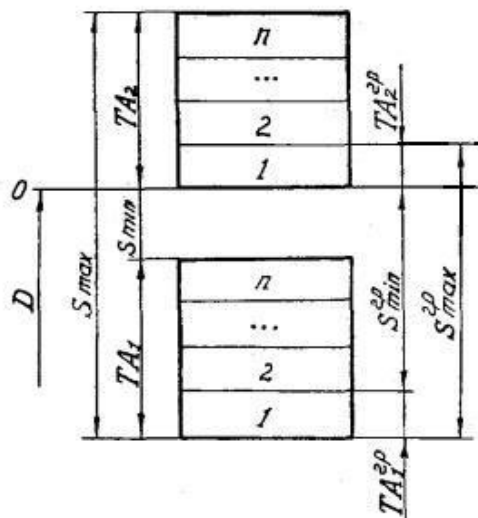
Схема полів допусків з'єднання із зазором
